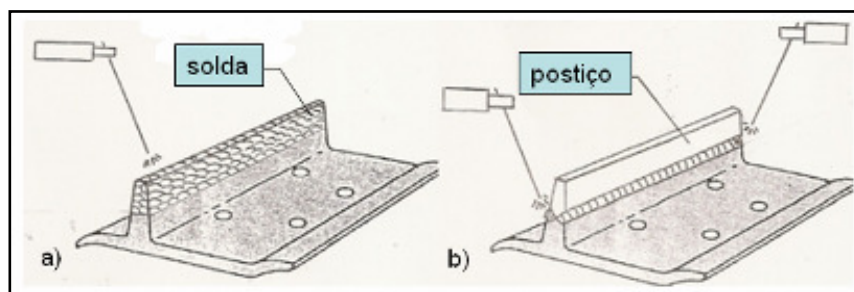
Exemplos de recuperação de sapatas: a) soldagem de enchimento; b) adição de postigo (adaptado de SOTREQ,2007)
